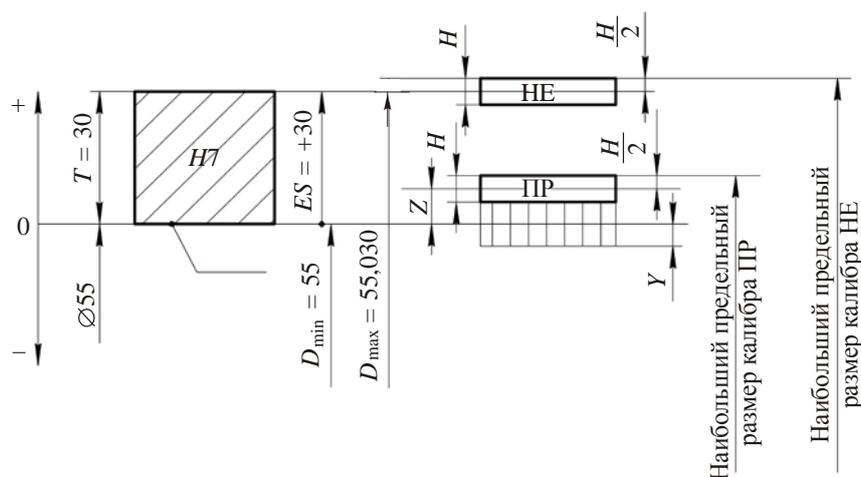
Схема расположения полей допусков рабочих калибров-пробок
